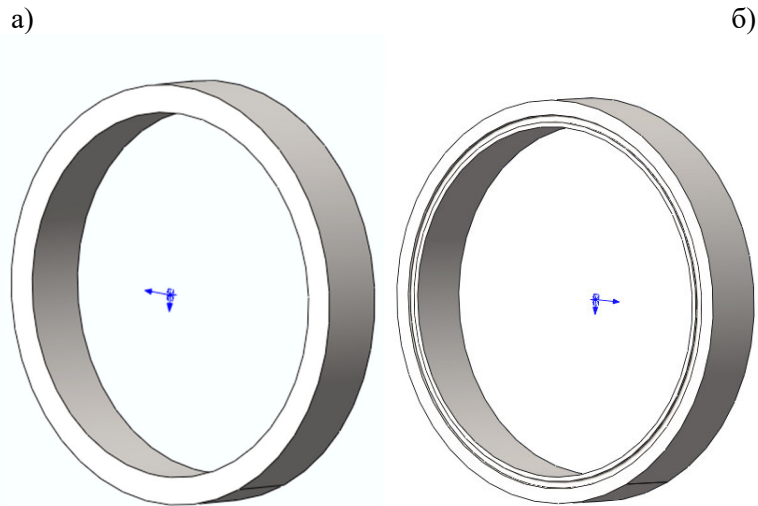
Объемные модели бандажа: а) плавающего типа (с прямоугольным сечением); б) сварного типа (с кольцевыми фасонными проточками)
